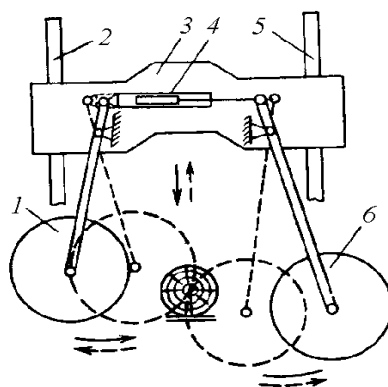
Комбинированный штангово-маятниковый пильный механизм
